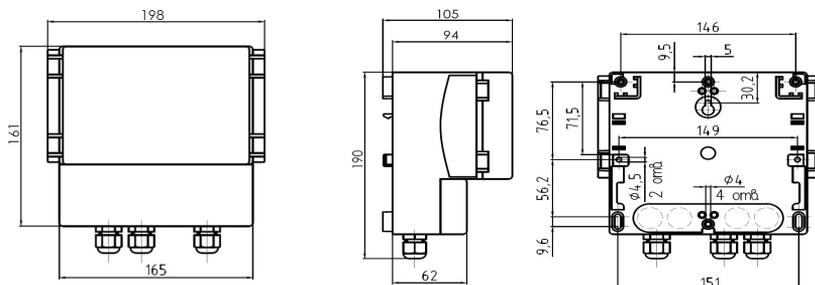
Габаритные и установочные размеры пластикового корпуса электронного преобразователя (невзрывозащищенного)
